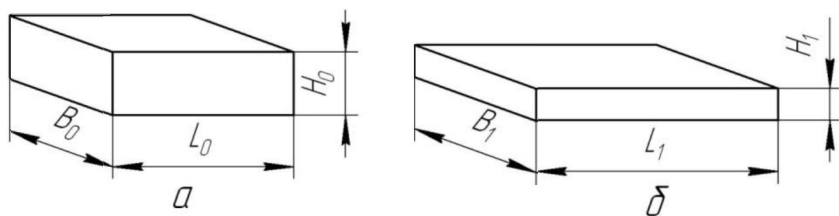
Размеры заготовки до (а) и после (б) прокатки
